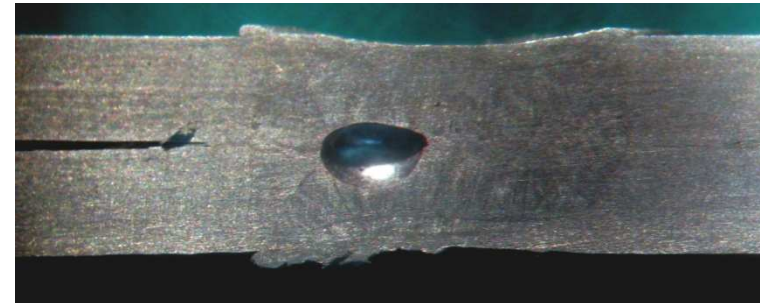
8. Macrografía del punto de soldadura en la probeta de 1 mm a 10x.
